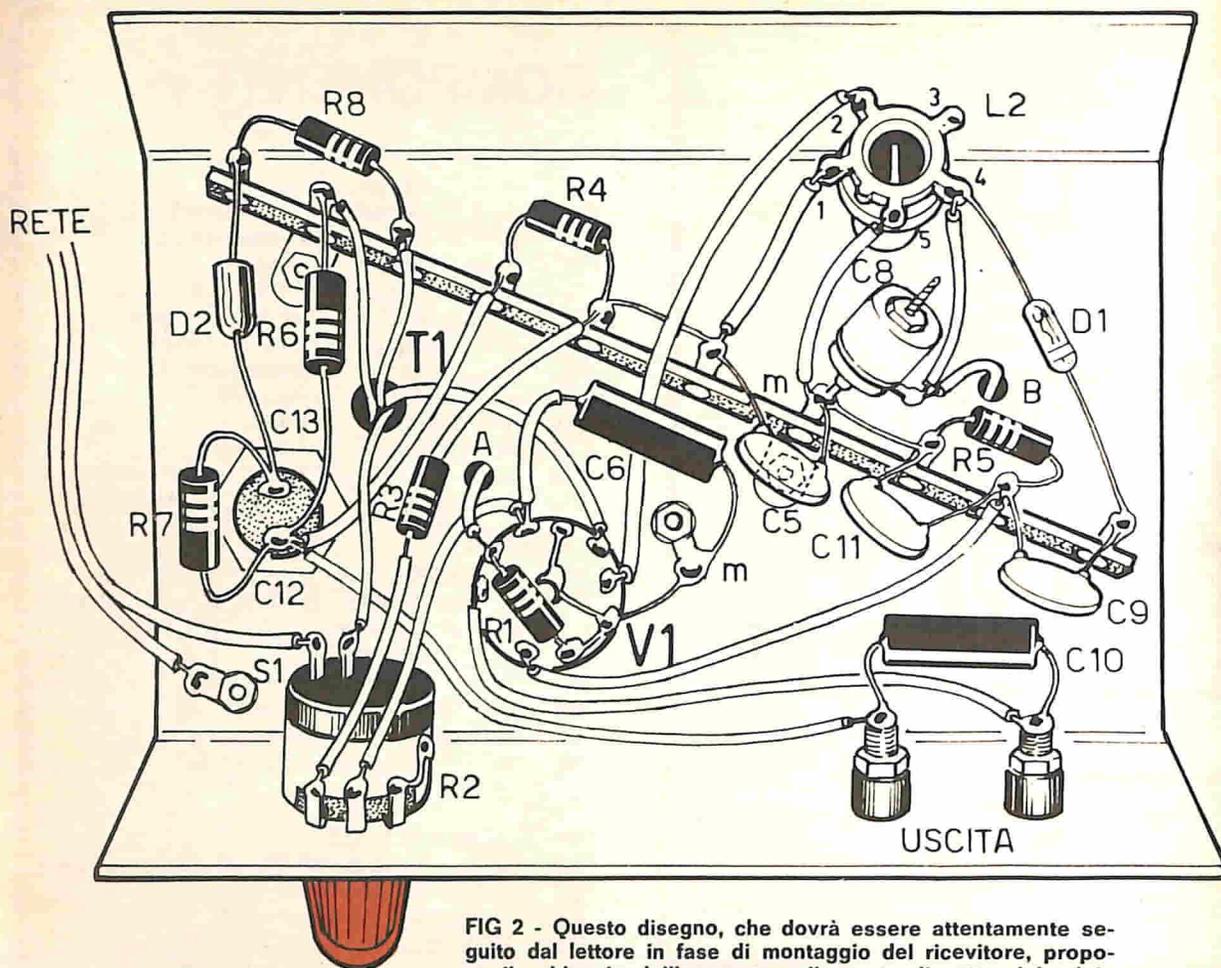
Questo disegno, che dovrà essere attentamente seguito dal lettore in fase di montaggio del ricevitore, propone il cablaggio dell'apparato nella parte di sotto del telaio metallico.
